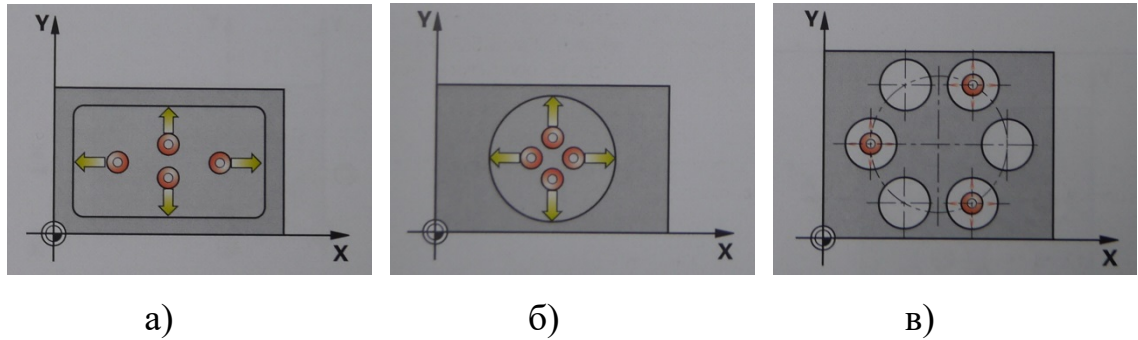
Приклади вимірювання розмірів заготовок на верстаті:
